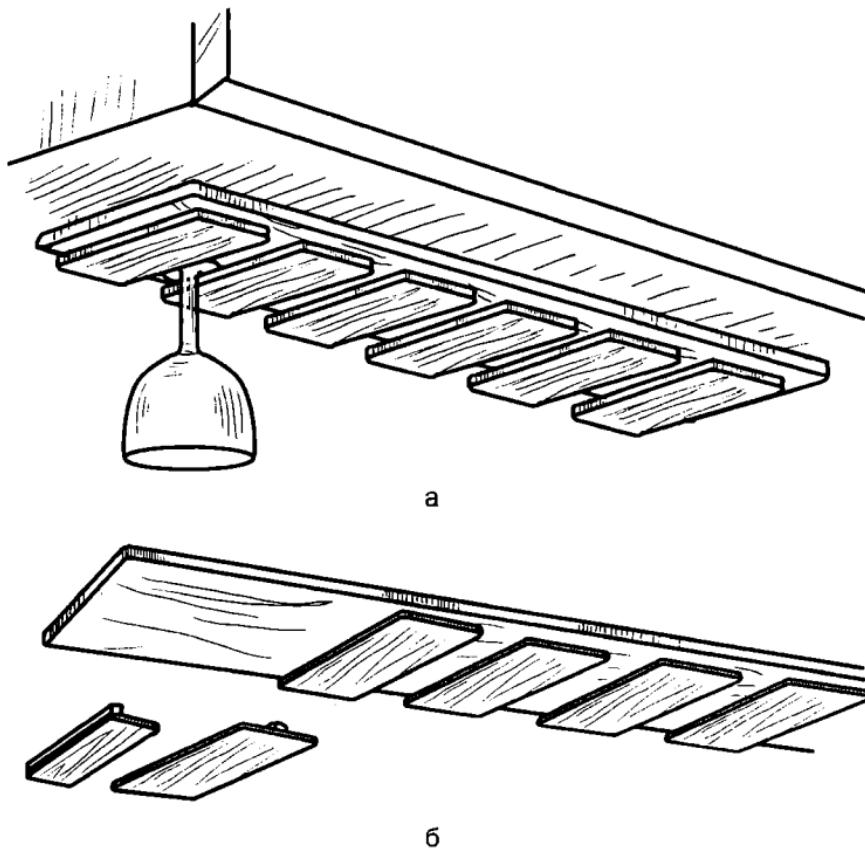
Полка-подвеска: а — общий вид; б — схема сборки
